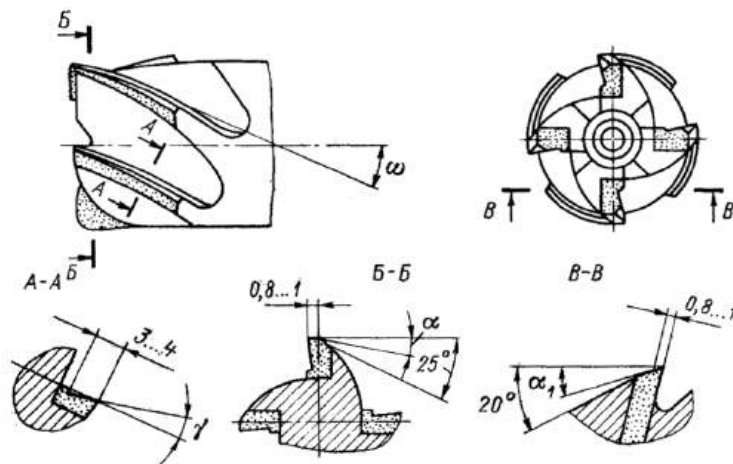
Типова конструкція твердосплавної кінцевої фрези
